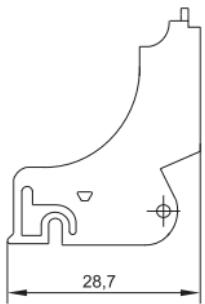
Габаритные и установочные размеры модуля / Figure 1 – Overall and mounting dimensions of the module / 1 сурет – Модулдің габариттік және орнату өлшемдері
